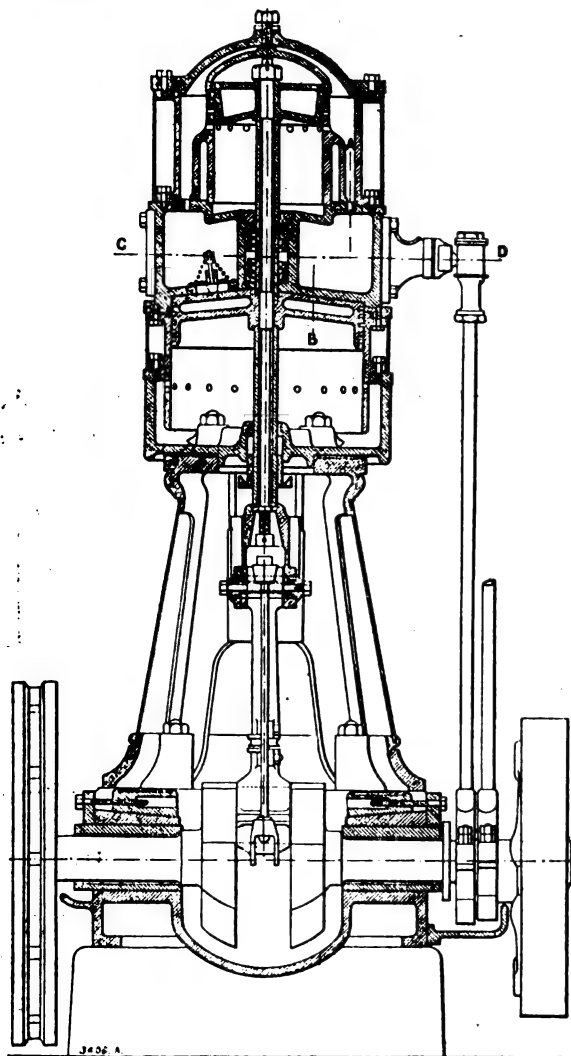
Coupe dans une machine à grande vitesse de M. Raworth faite par un plan vertical passant entre les deux soupapes de régulation.
